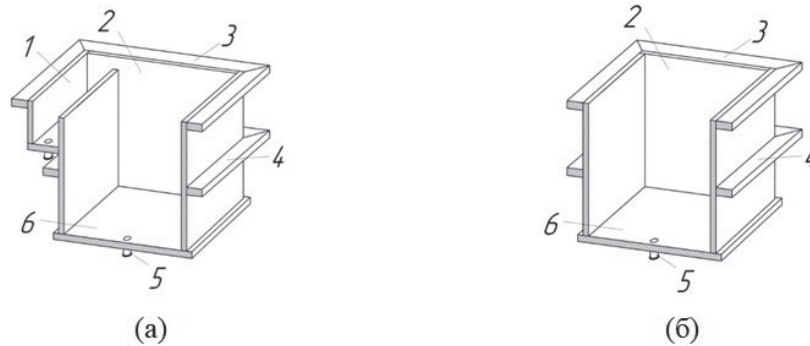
Корпус ванны: (а) – корпус ванны с карманом; (б) – корпус ванны без кармана. 1. – карман; 2. – стенка; 3. – отбортовка; 4. – оребрение; 5. – сливной патрубок; 6. – дно
